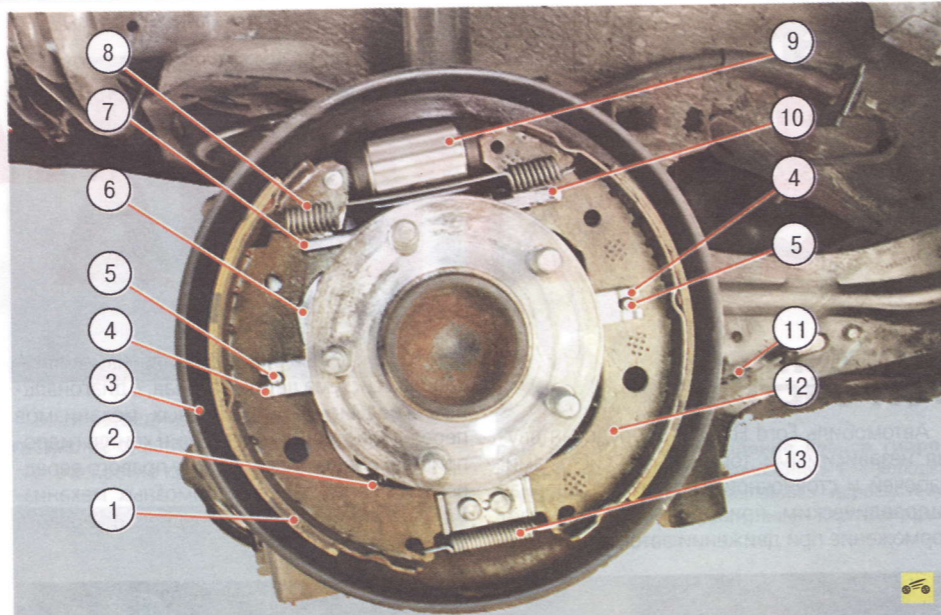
Тормозной механизм заднего колеса: 1 – задняя тормозная колодка; 2 – наконечник троса привода стояночного тормоза; 3 – щит тормозного механизма; 4 – прижимные скобы тормозных колодок; 5 – опорные стойки; 6 – разжимной рычаг привода стояночного тормоза; 7 – распорная планка; 8 – верхняя стяжная пружина; 9 – рабочий цилиндр; 10 – регулятор зазоров; 11 – трос привода стояночного тормоза; 12 – передняя тормозная колодка; 13 – нижняя стяжная пружина
